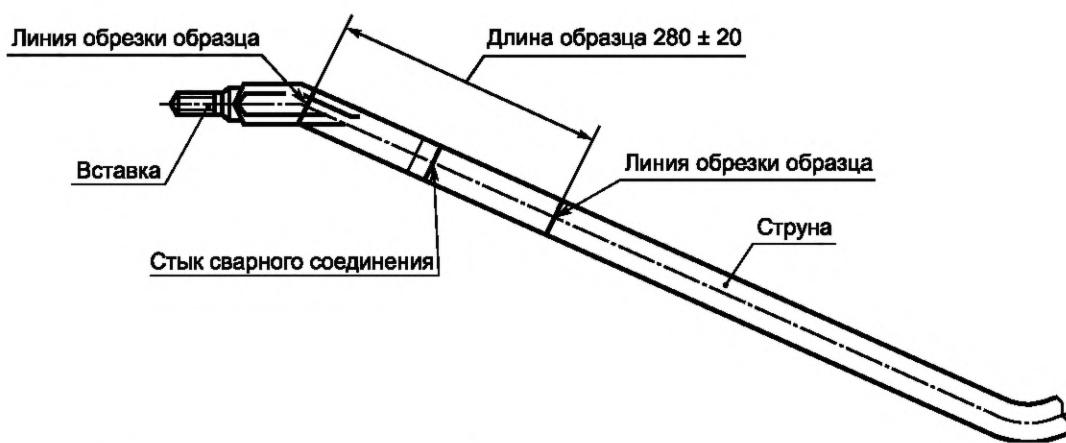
Схема вырезки образца для испытания сварного соединения, выполненного контактной стиковкой сваркой
